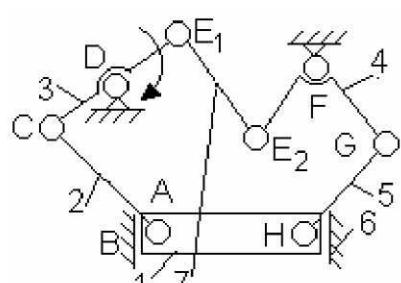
Схема механизма двухкривошипного пресса
